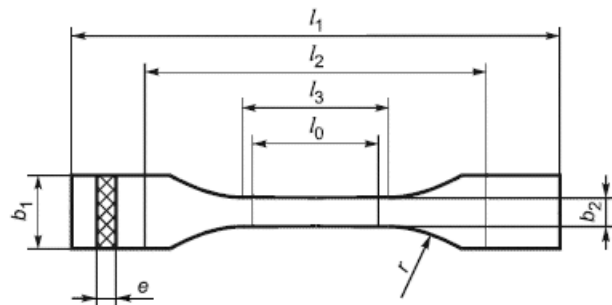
Образец типа 2А, изготавливаемый механической обработкой
